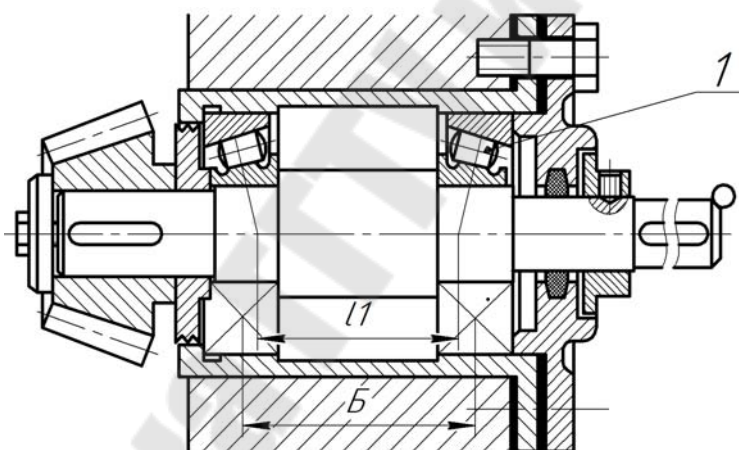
Подшипниковый узел на конических роликоподшипниках
